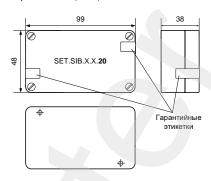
Внешний вид, габаритные и установочные размеры счётчика SET.SIB.X.X.20
